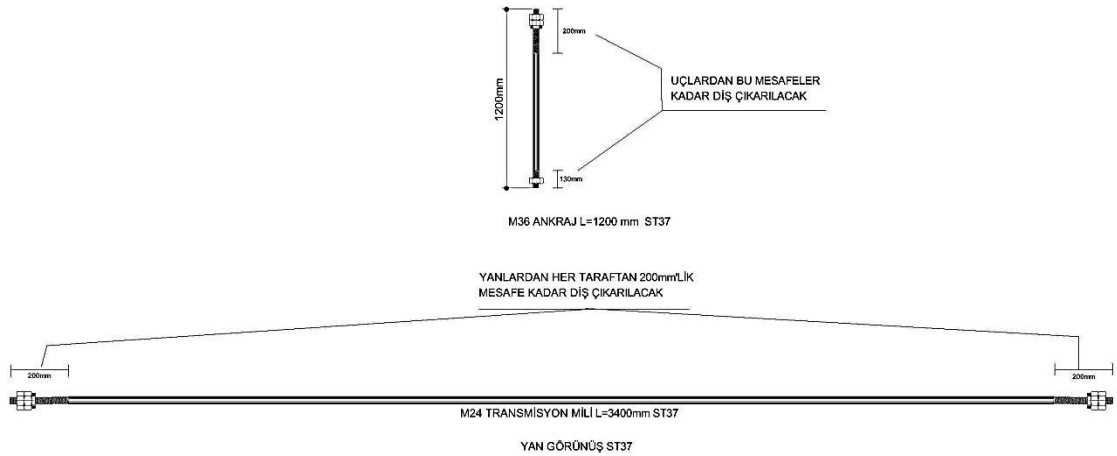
Eksenel Yükleme Çerçevesi Planı [51, 58]
